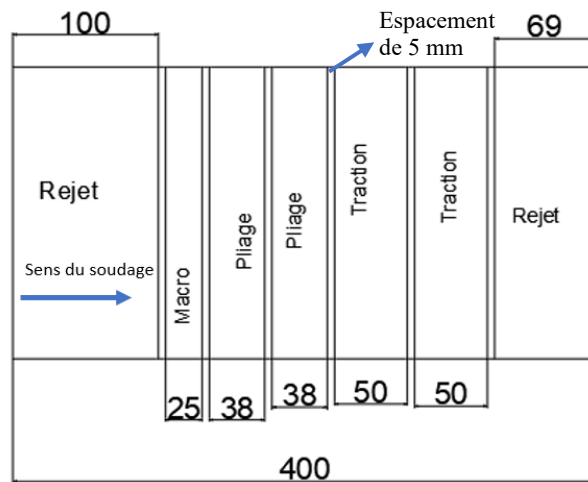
Plan d'usinage pour les tests de qualification (dimensions en mm)
